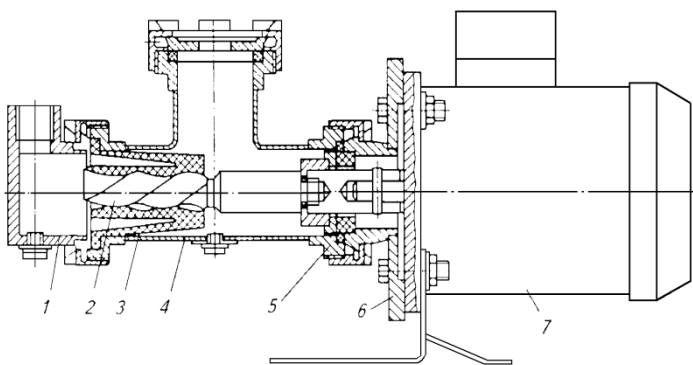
Общий вид одновинтового электронасосного агрегата марки П8-ОНВ: 1-крышка; 2- винт; 3-статор (обойма); 4-корпус насоса; 5-фланец; 6-основание; 7-электродвигатель.
